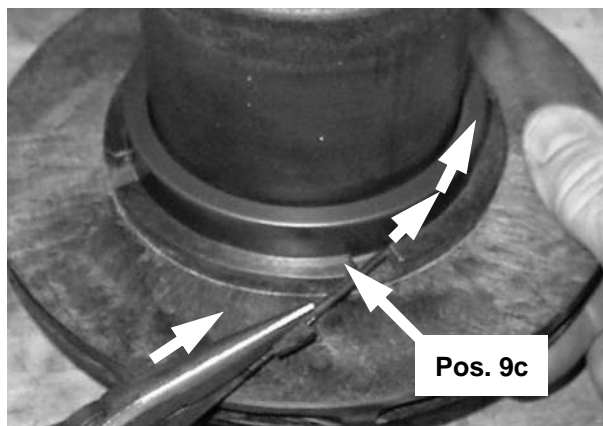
Eins. des hinteren rot. Schleißrings
